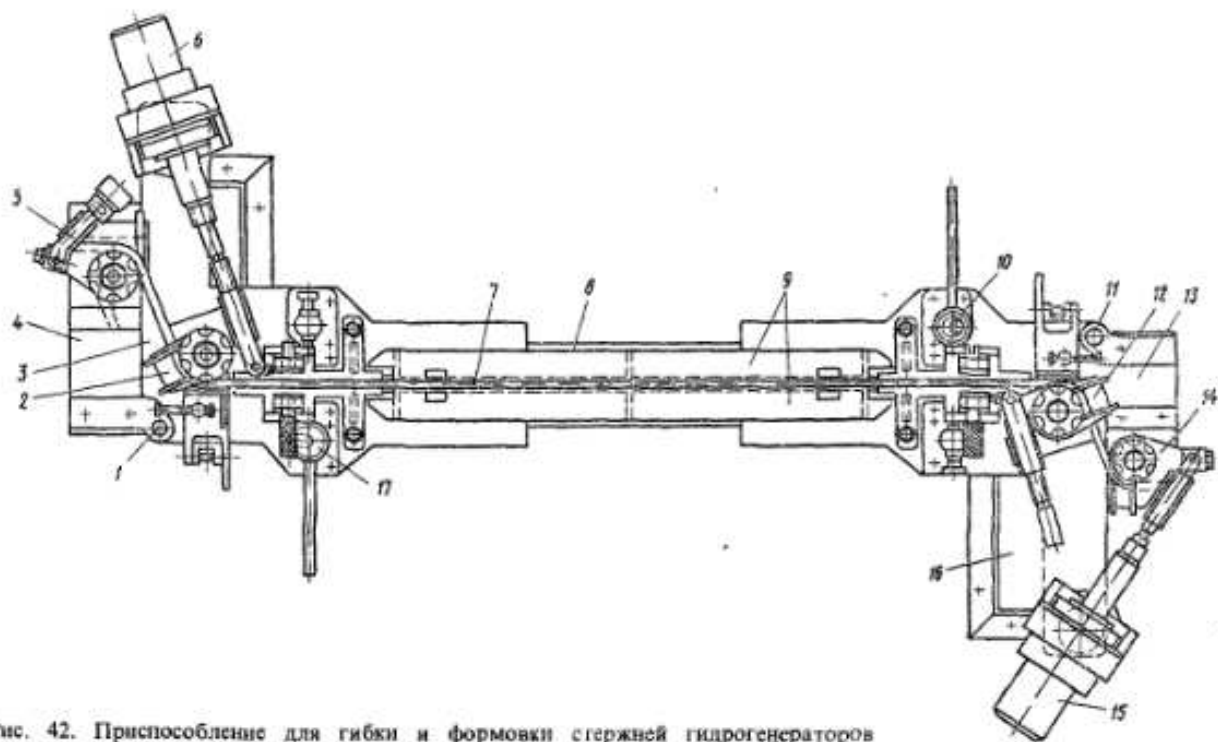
Приспособление для гибки и формовки стержней гидрогенераторов
